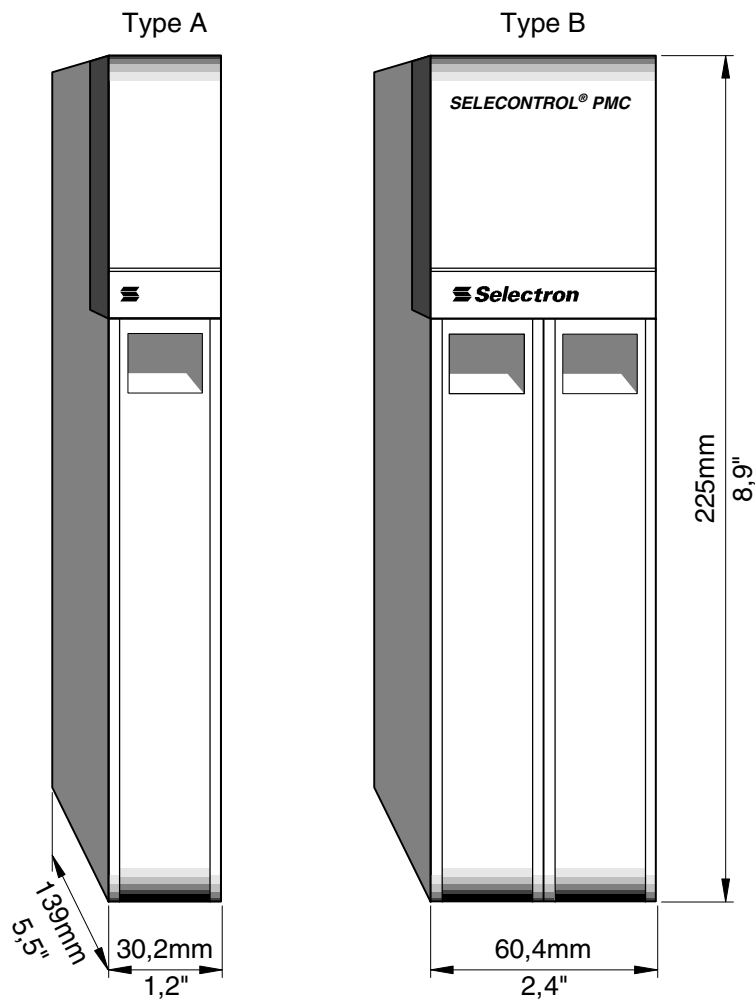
/2 Masszeichnung der beiden Baugruppentypen A/B
